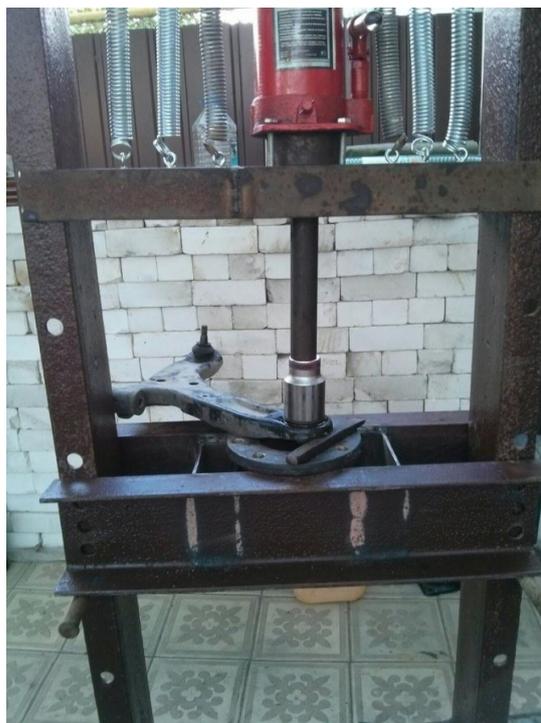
пресс для запрессовки и выпрессовки сайлентблоков
